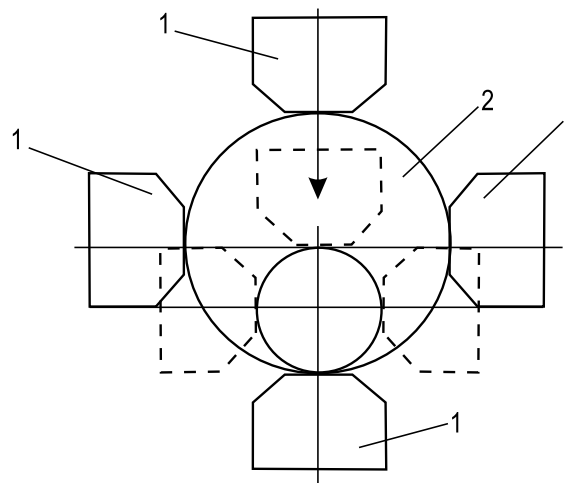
Схема деформации заготовки с макросдвигами (поперечное сечение): 1 – бойки, 2 – заготовка.
